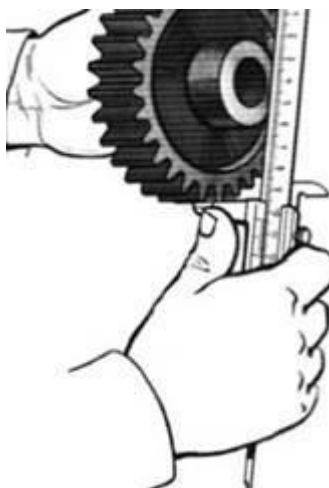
Измерение диаметра окружности вершин зубьев зубчатого колеса
